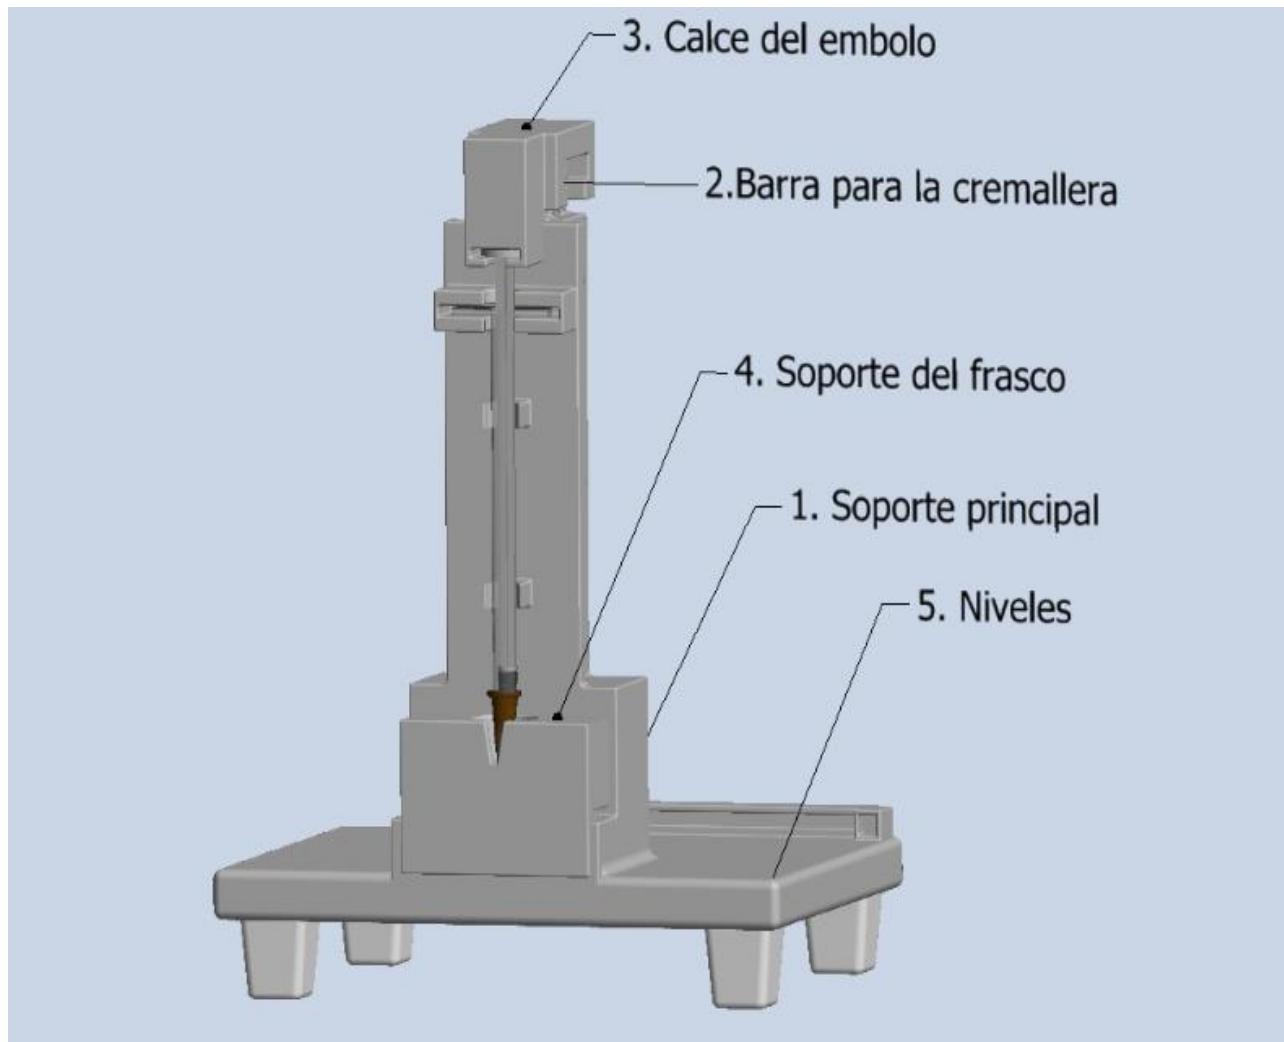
Estructura Mecánica sin cremallera, engranaje y soporte del motor. Diseñado en inventor [5].
